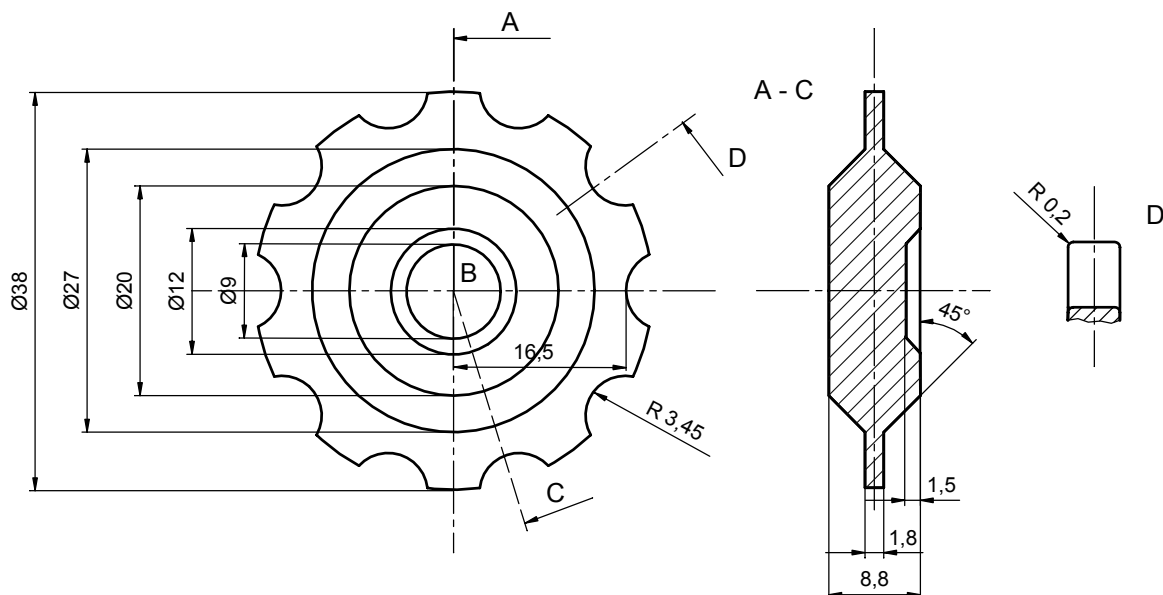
Konstruktionszeichnung des Realbauteils „Laufrolle“
